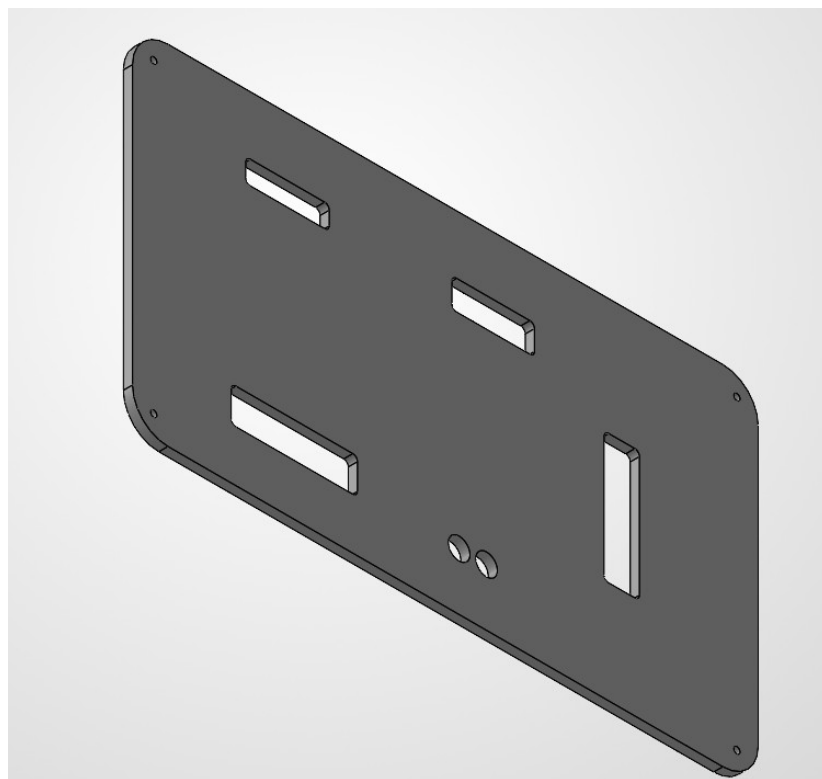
Верхня кришка корпусу, ізометричний вигляд
